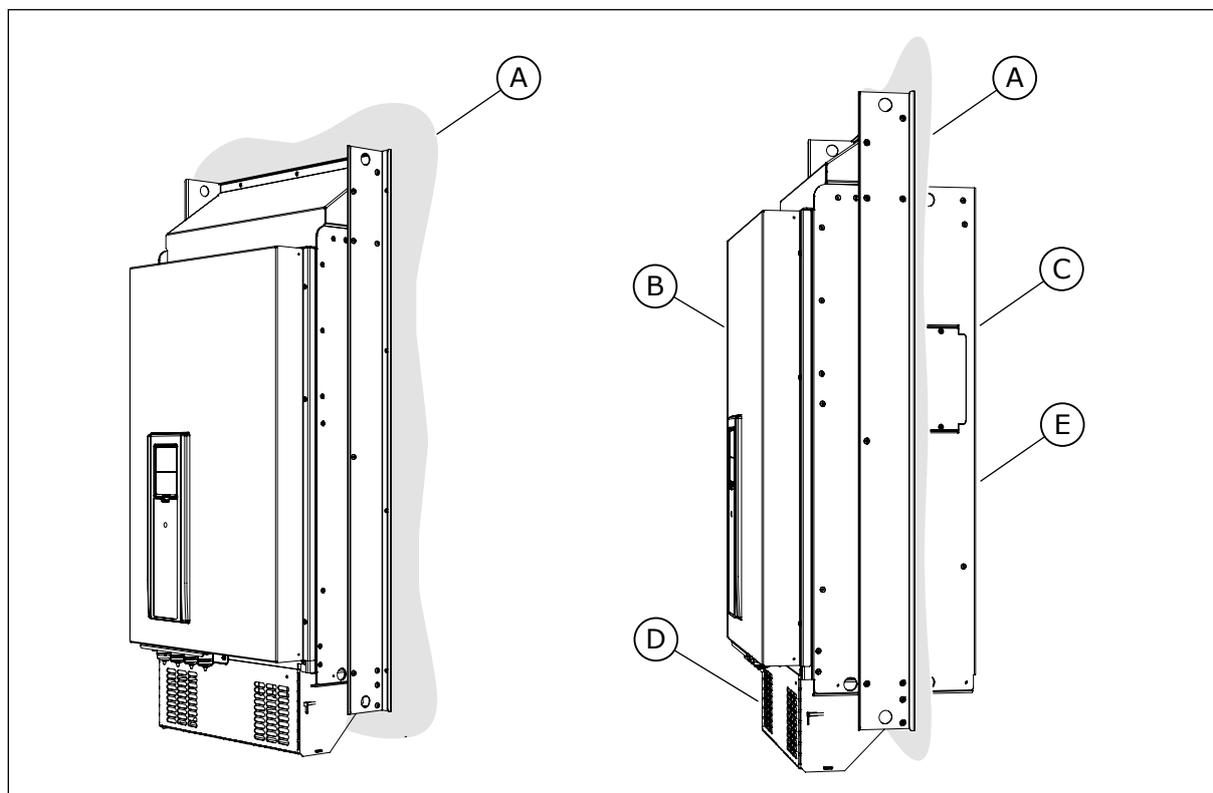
Exemplo de montagem em flange (chassi MR9)
